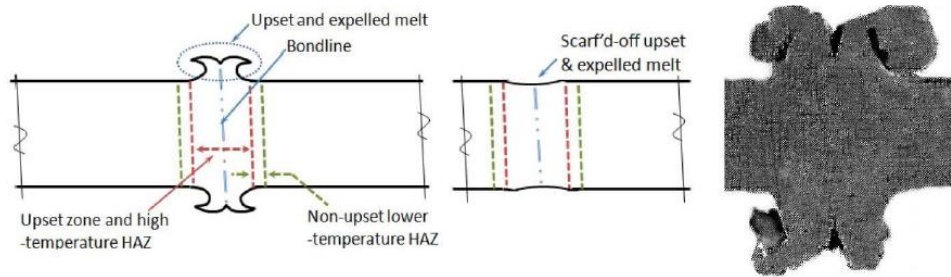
Vista del eje de la soldadura antes y después del maquinado [2]
